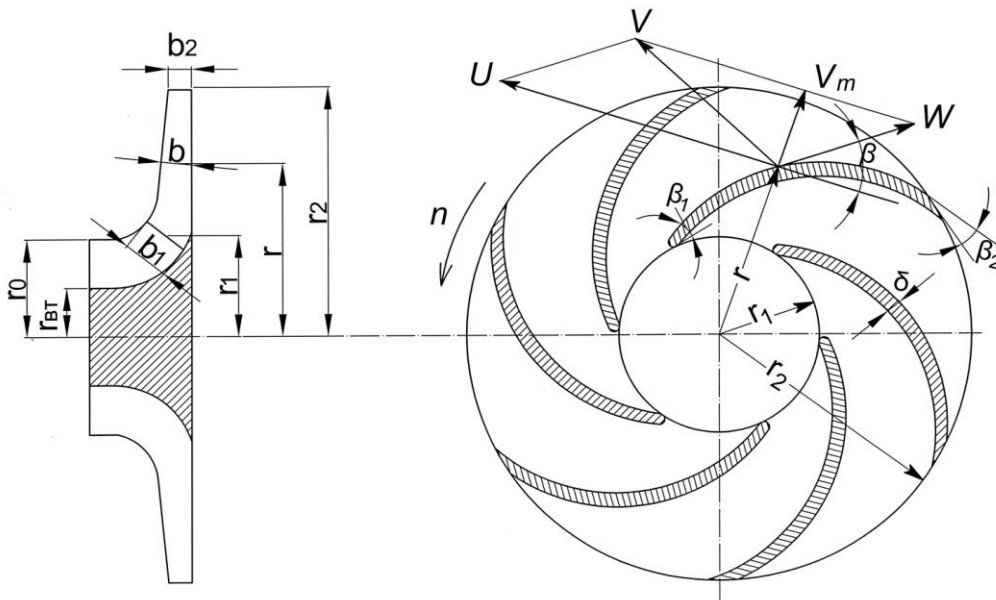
Схематический разрез рабочего колеса центробежного насоса
